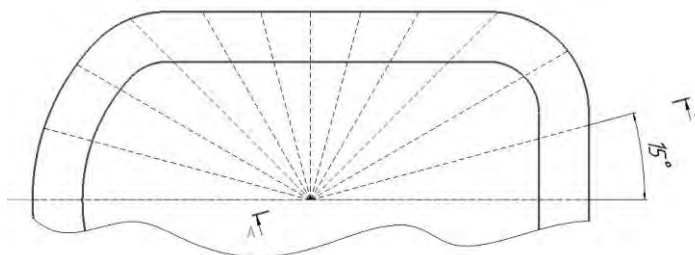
Эскиз детали в полярных координатах (вид сверху)
